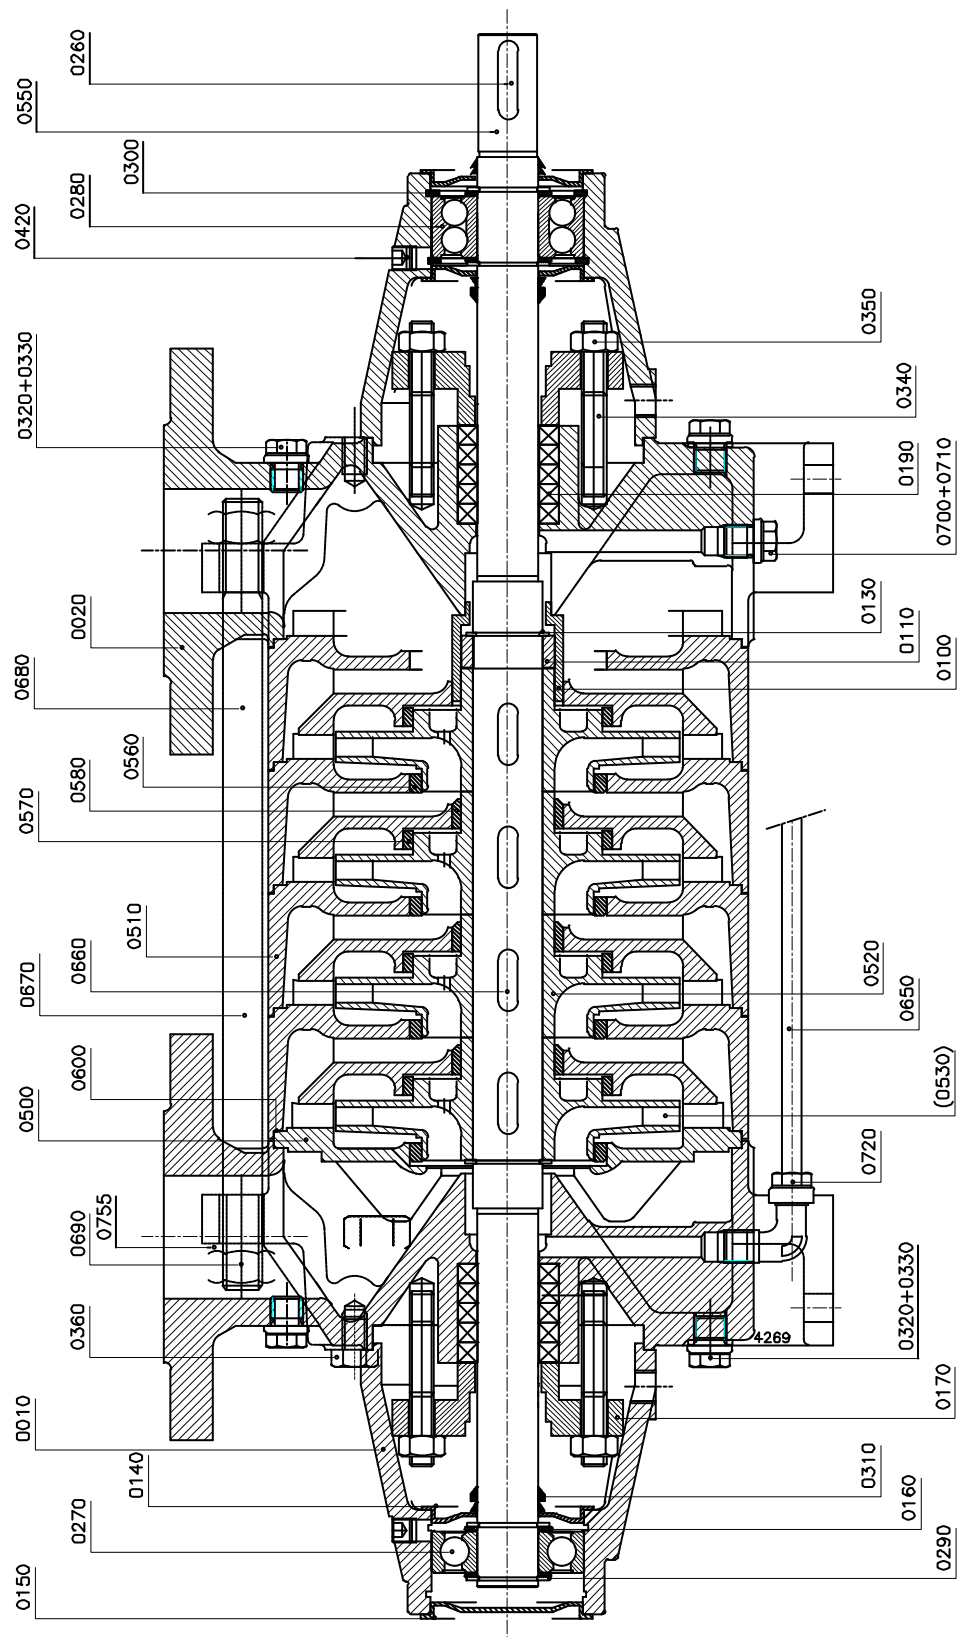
MCHS 14a/b med tung lagerkonstruksjon.
